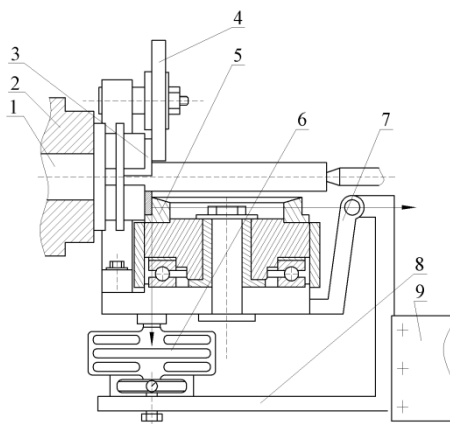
Схема вимірювання радіального зусилля: 1-циліндрична ступінчаста оправа; 2-токарний патрон; 3-заготовка; 4-притискний ролик; 5-формуючий ролик; 6-динамометр; 7-баланси́р; 8-рама; 9-супорт верстату
